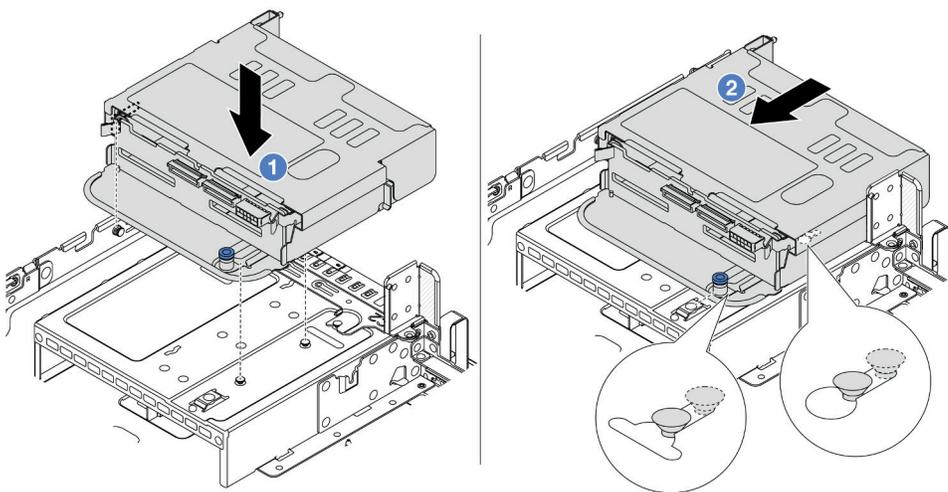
Installation du boîtier d'unités de disque dur arrière 4 x 2,5 pouces
